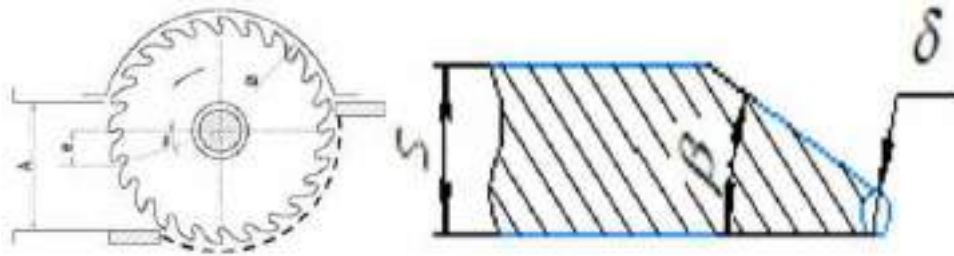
Схема роботи робочого органу: а) схема взаємодії леза із деревиною; б) схема зношування ножа. 1 - лезо; 2 - деревина; 3 - протиризальна пластина; k - зазор в ріжучій парі.
